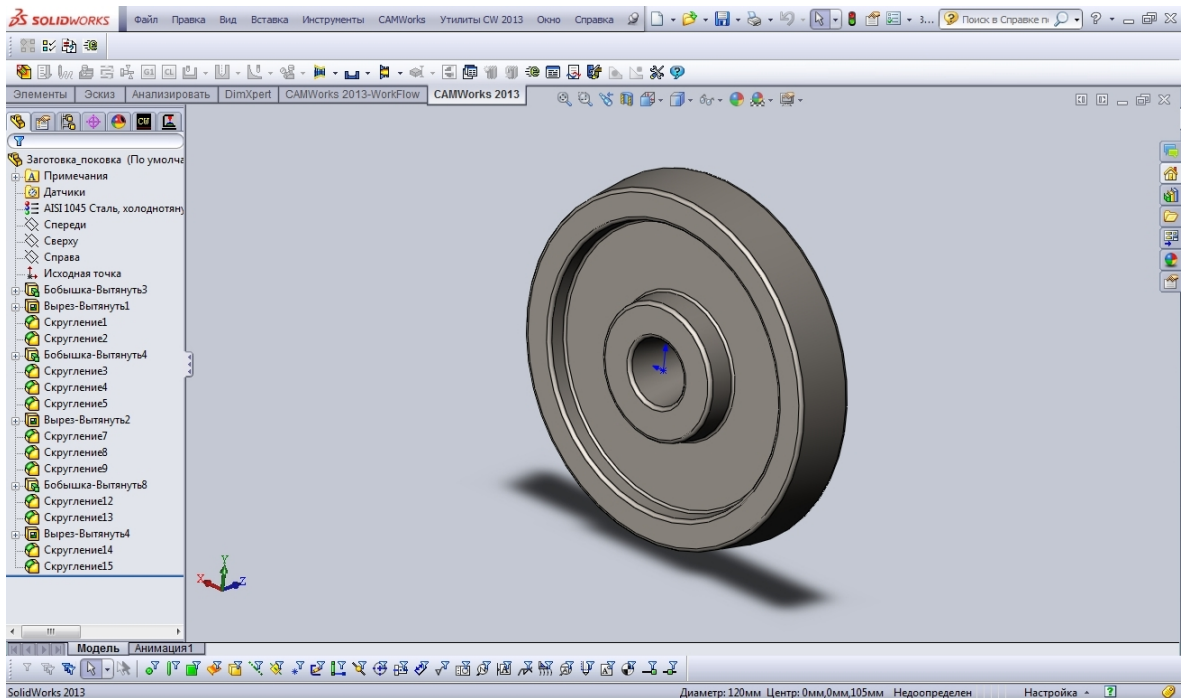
Модель заготовки (поковка) «Колесо ТП 05.22.05.196.003» з деревом побудови
